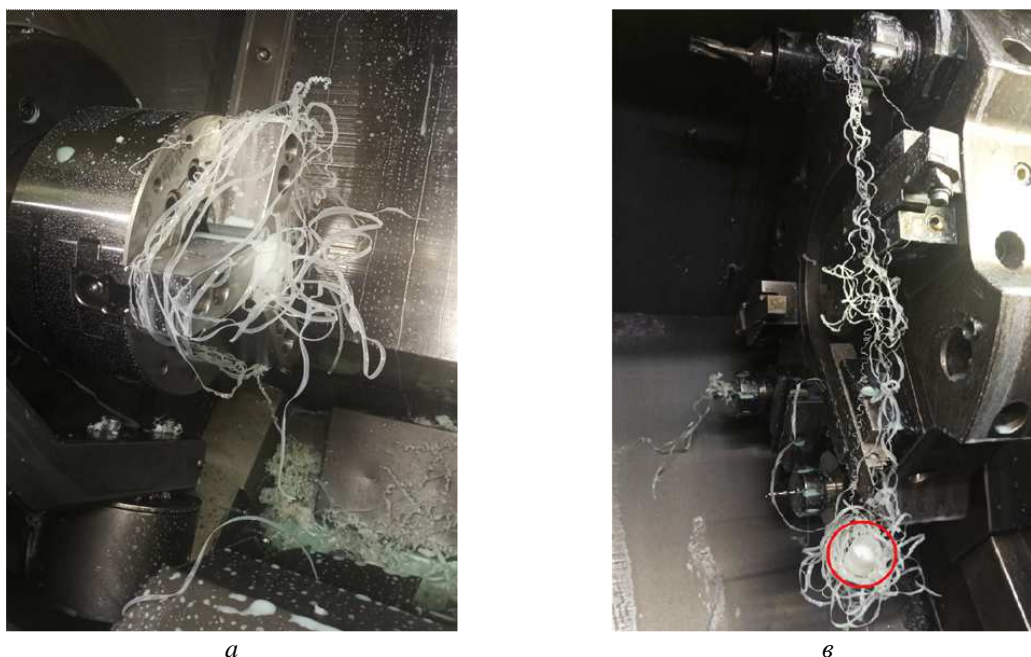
Наматывание стружки при точении капролона на: а) патрон, кулачки и заготовку; б) револьверную головку, инструмент и деталь
